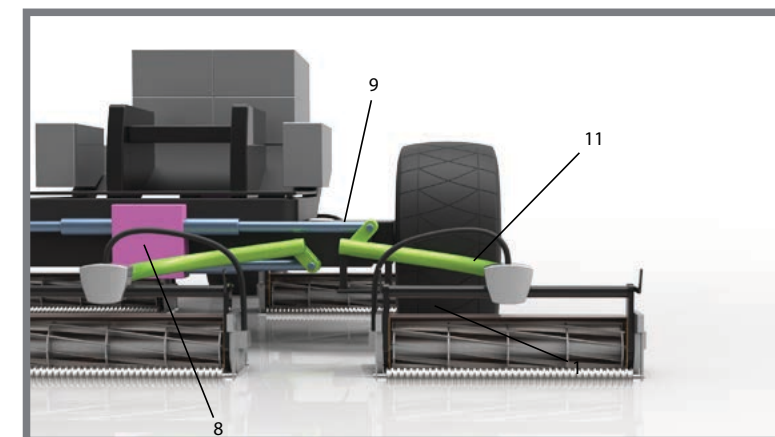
Finální technické řešení - ovládání sekacích jednotek
